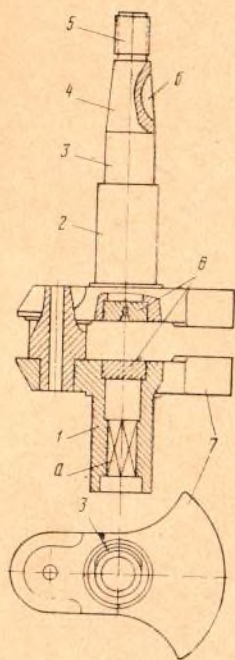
Составной коленчатый вал одноцилиндрового двигателя
